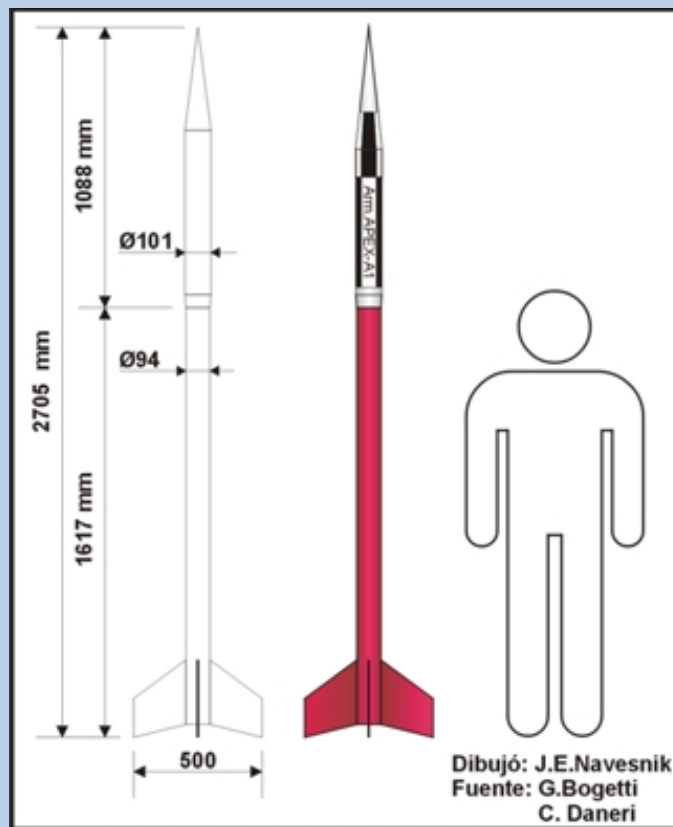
Dimensiones del cohete Alfa Centauro
